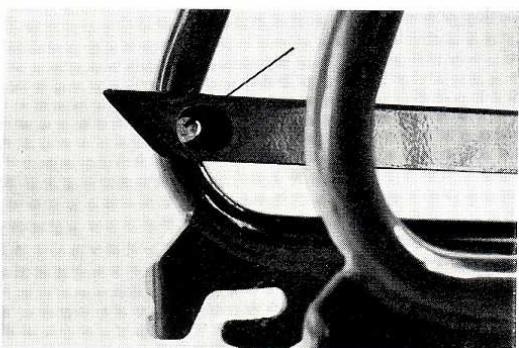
DEMONTAGE DU GARDE-CHAINE.
